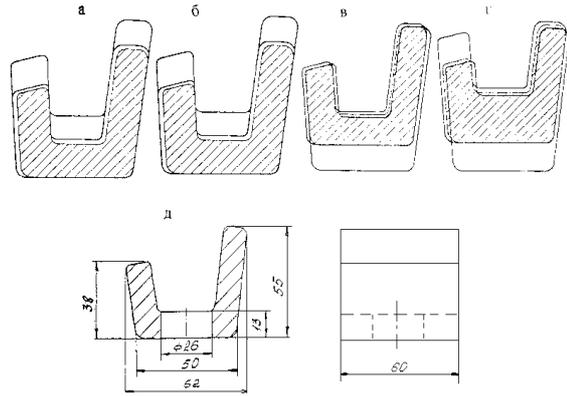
Схема взаимодействия ножей и профиля в процессе рубки (а, б, в, г); чертёж отрезаемой заготовки (д)
